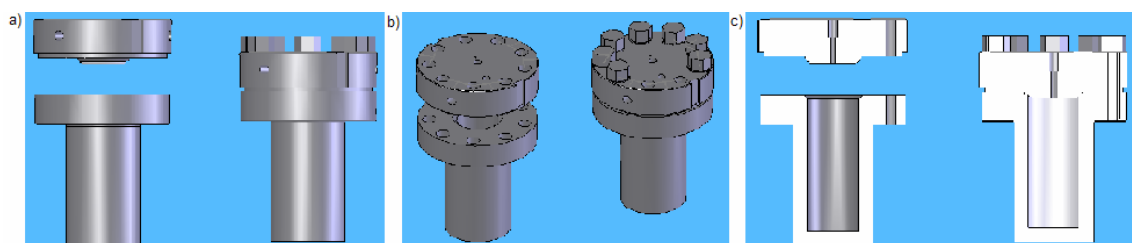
Reator a) vista frontal, do reator montado e da tampa e copo separados. b) vista isométrica c) vista em corte.
